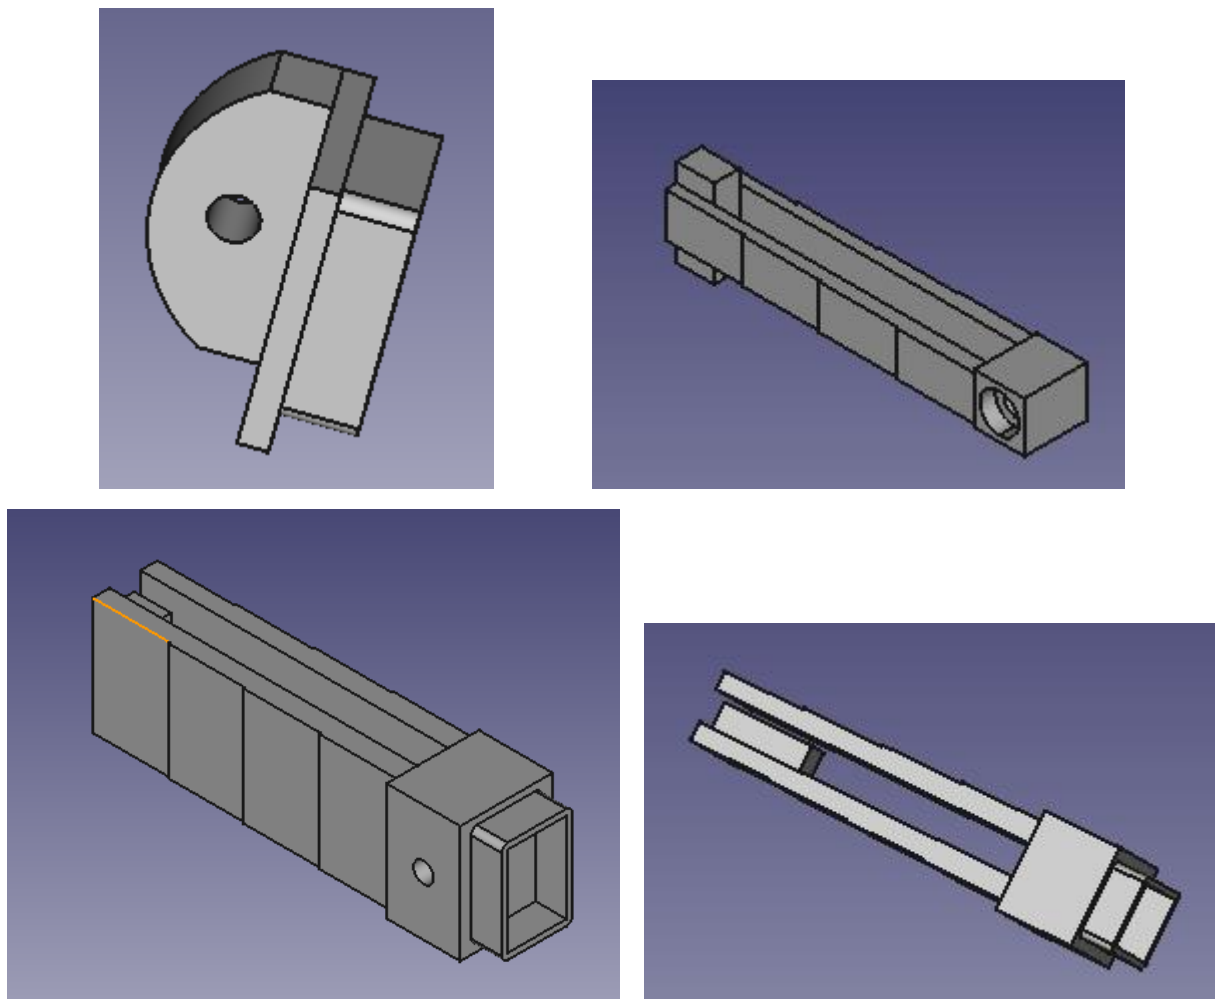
Conjunto de piezas diseñadas para el soporte de la bobina del Tag.
